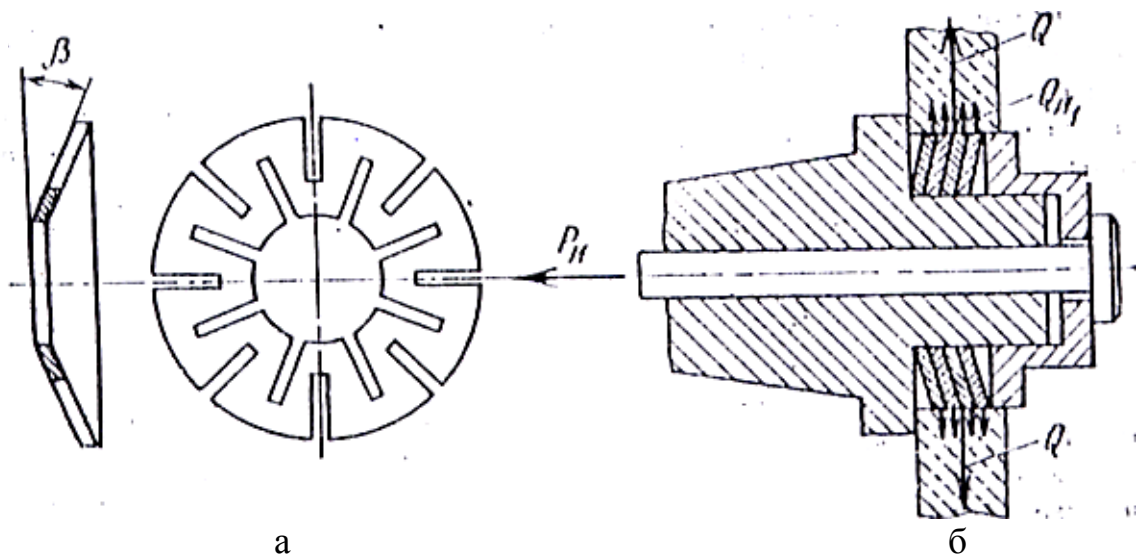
Силовые механизмы с пластинчатыми пружинами: а - пружина; б - закрепление заготовки на оправке с пластинчатыми пружинами.
